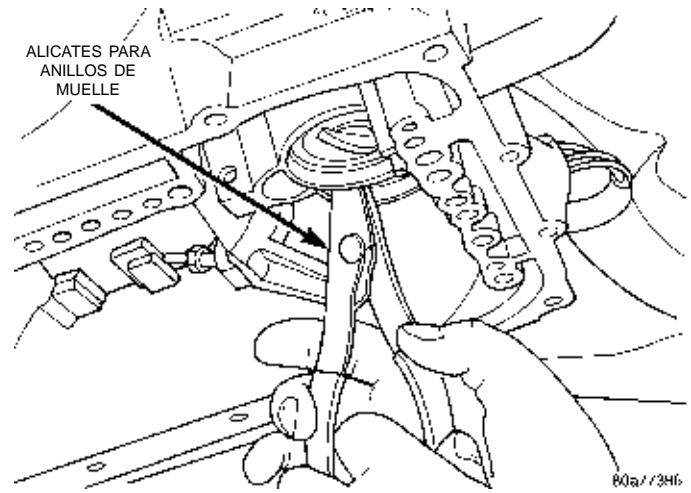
Anillo de muelle del soporte del engranaje anular delantero
